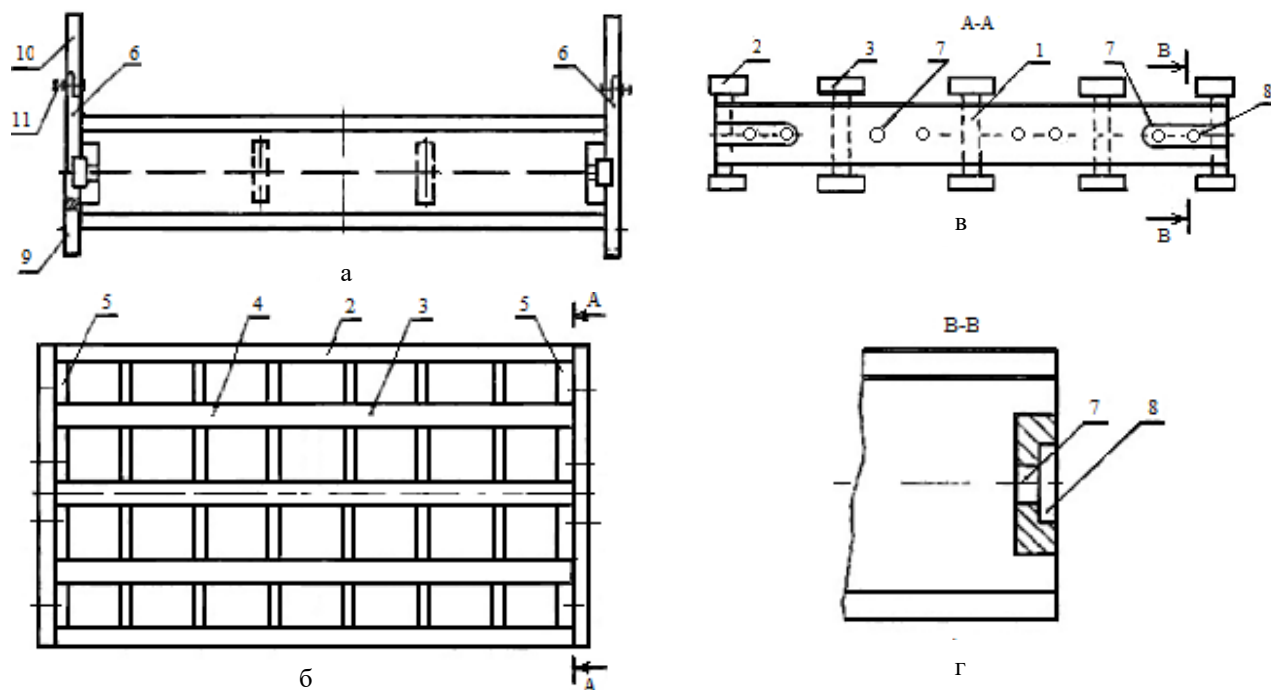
Прокатно-сварная спекательная тележка с переворачиваемым корпусом
